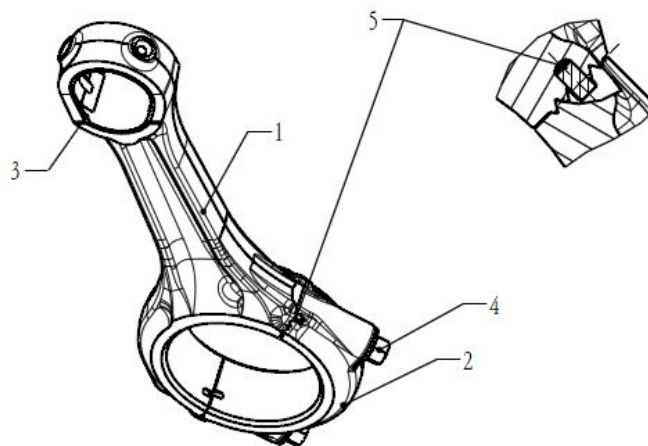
Расположение корпуса шатуна 16М33 и крышки шатуна
